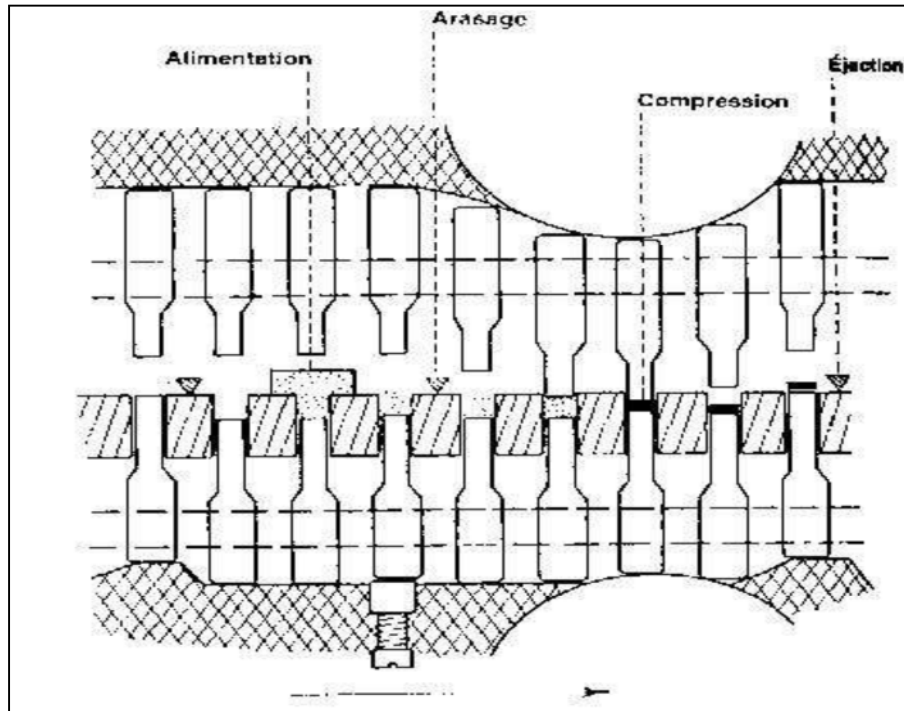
Schéma du principe de la compression sur machine à comprimer rotative [14].
